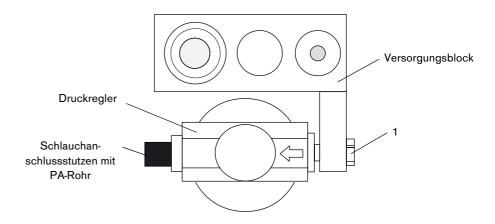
Ansicht auf den Versorgungsblock, Schraube entfernen
